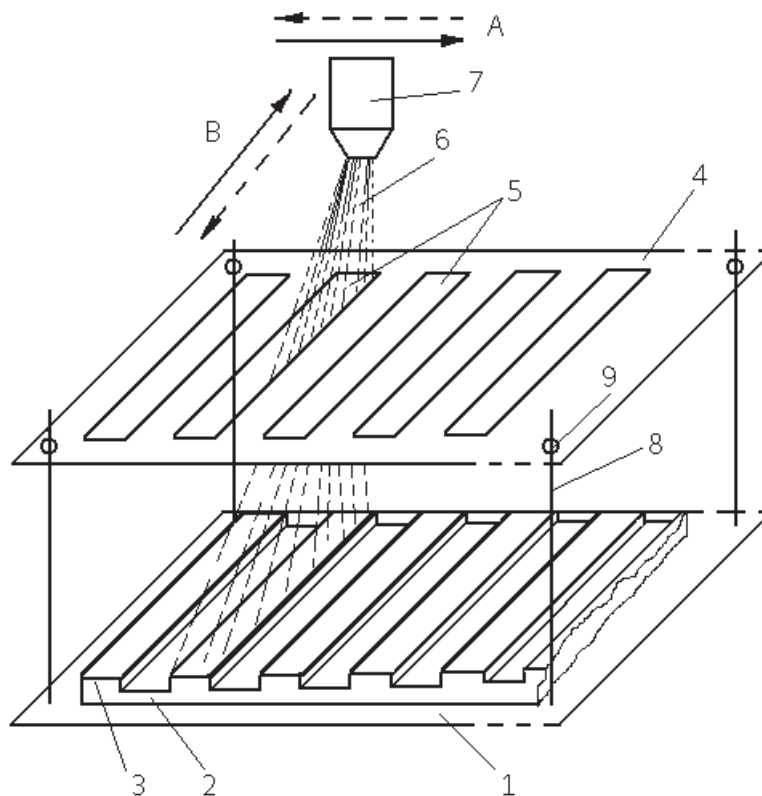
Процесс изготовления сердечника индуктора ЛИД
